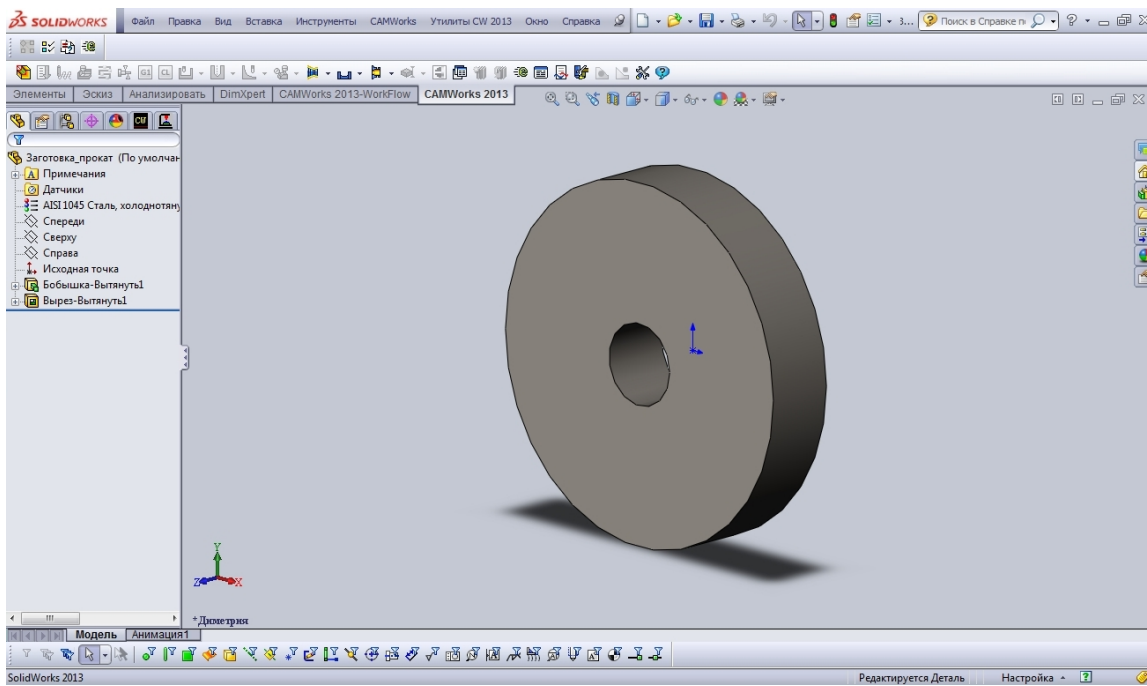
Модель заготовки (прокат) «Колесо ТП 05.22.05.196.003» з деревом побудови
